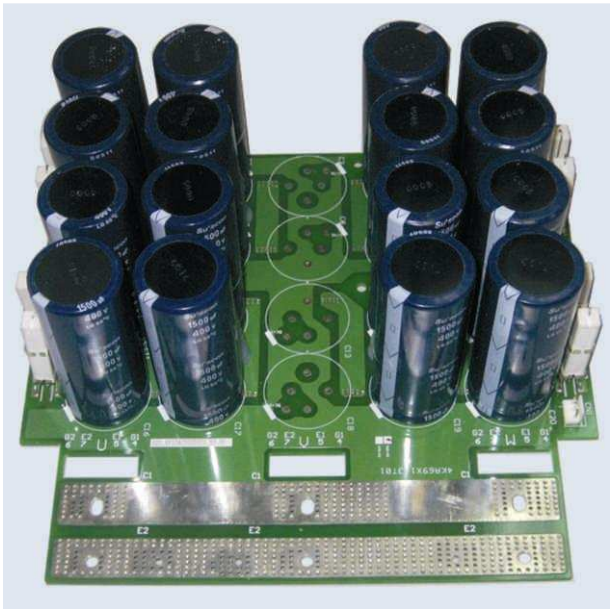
Фото общего вида преобразователей E2-8300-060H, -075H.
